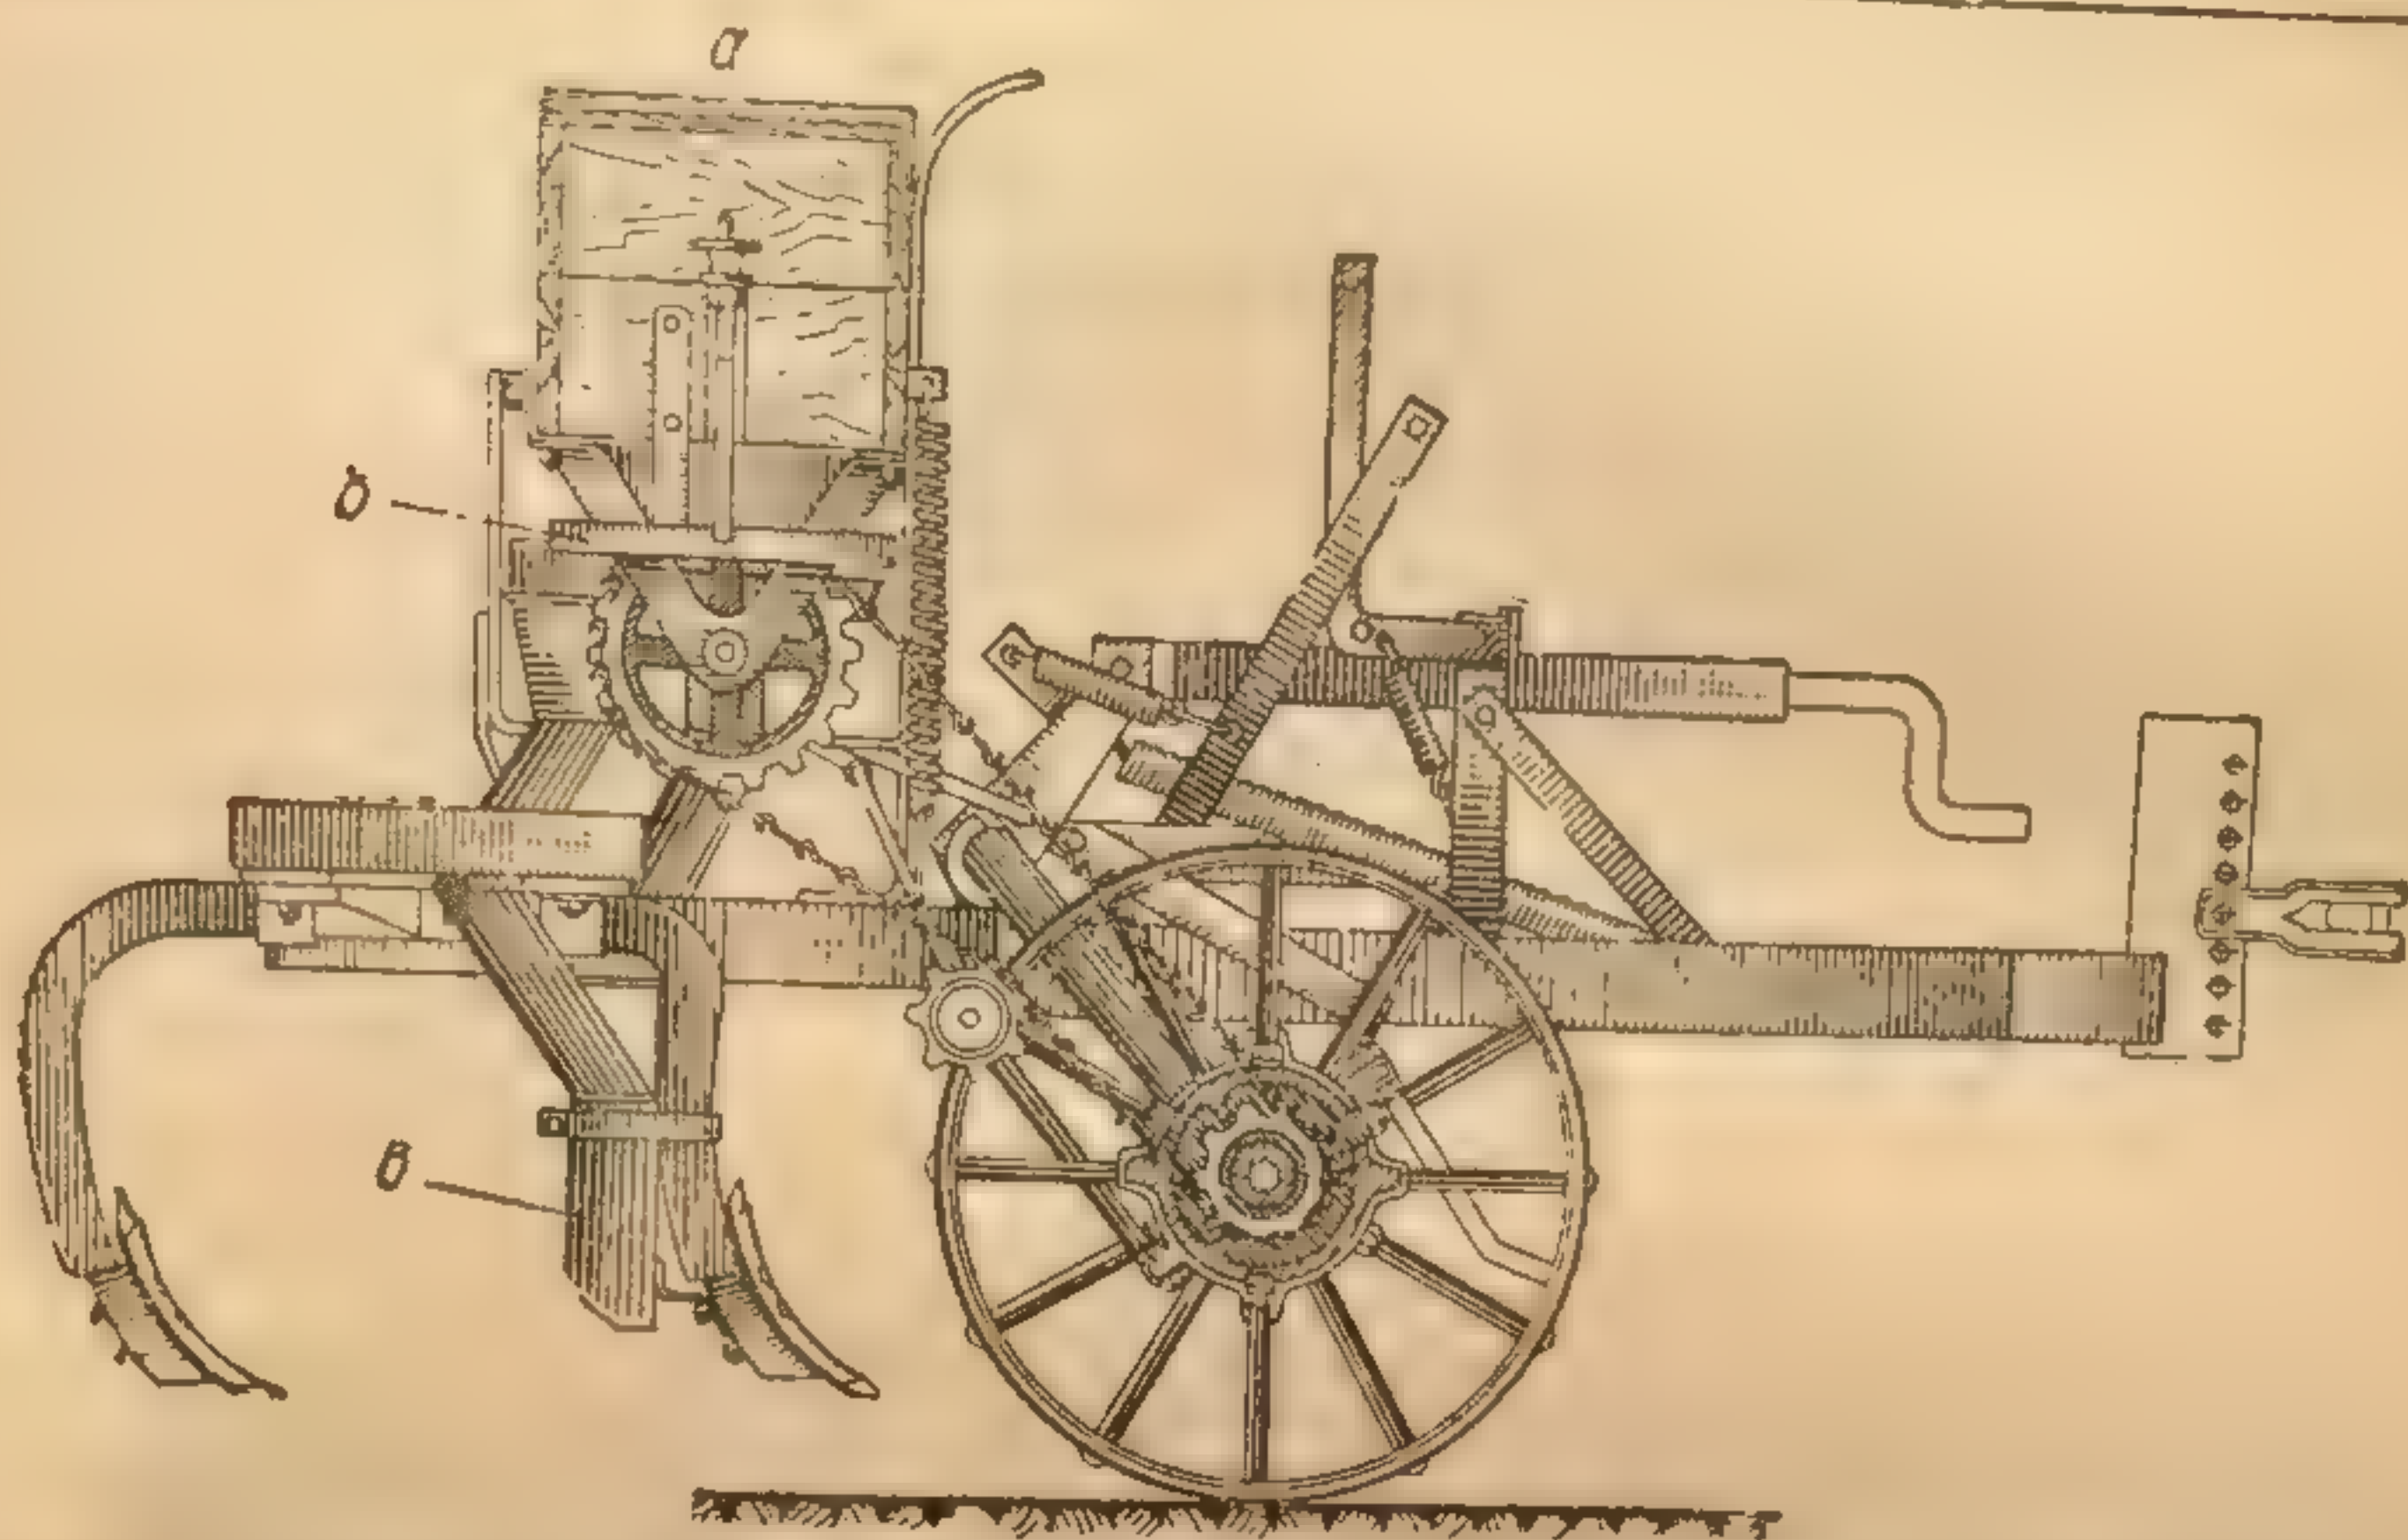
Приспособление УГ на чизель для глубокого внесения удобрений при глубокой обработке почвы, без оборота пласта:
